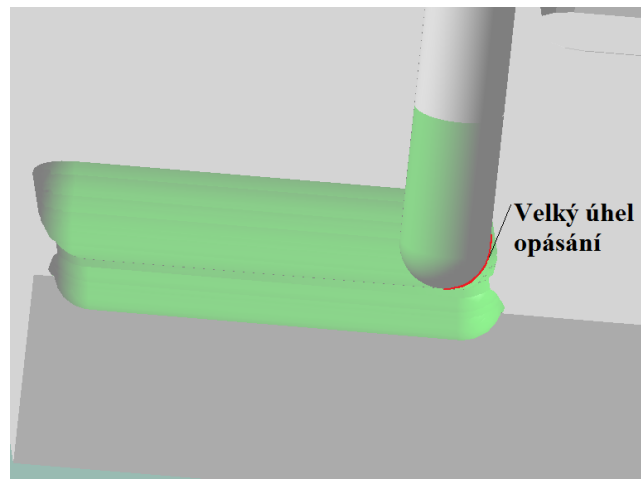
Nástroj 5 po 8 minutách obrábění
